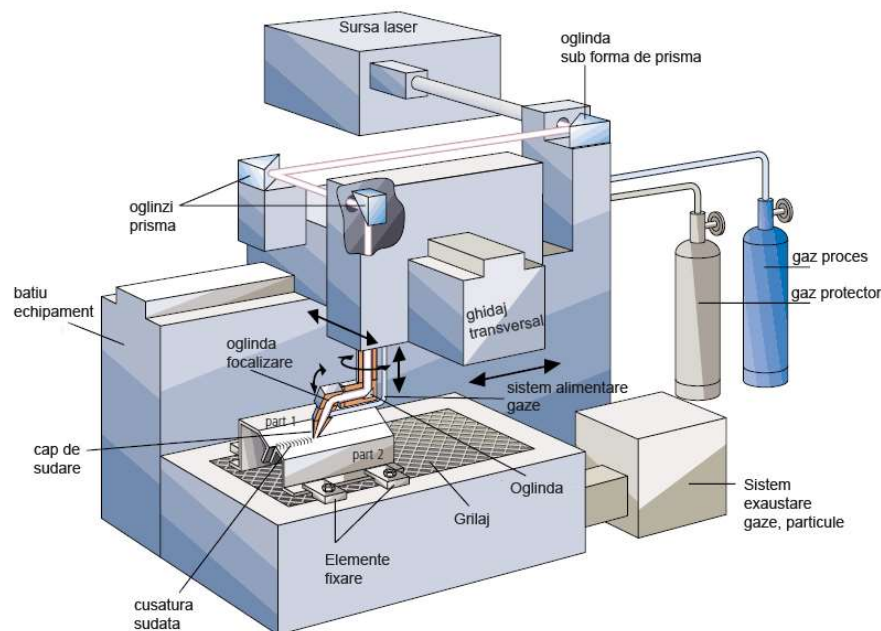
Schemă de principiu a unei instalații de sudare cu laser [33].
